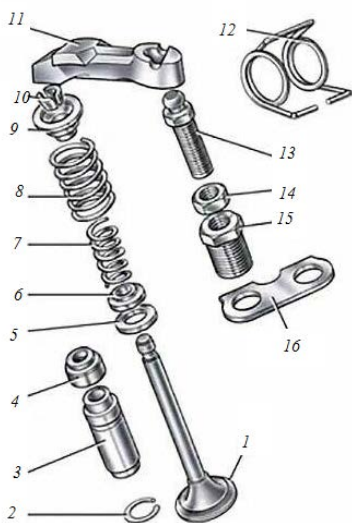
Детали клапанной группы и привода клапанов: 1 – клапан; 2 – стопорное кольцо направляющей втулки; 3 – направляющая втулка; 4 – сальник клапана; 5, 6 – опорные шайбы внутренней и внешней пружины; 7, 8 – внутренняя и внешняя возвратные пружины; 9 – тарелка пружины; 10 – сухари; 11 – рычаг привода клапана; 12 – пружина рычага; 13 – упорный винт; 14 – контргайка упорного винта; 15 – втулка упорного винта; 16 – стопорная пластина пружины рычага
